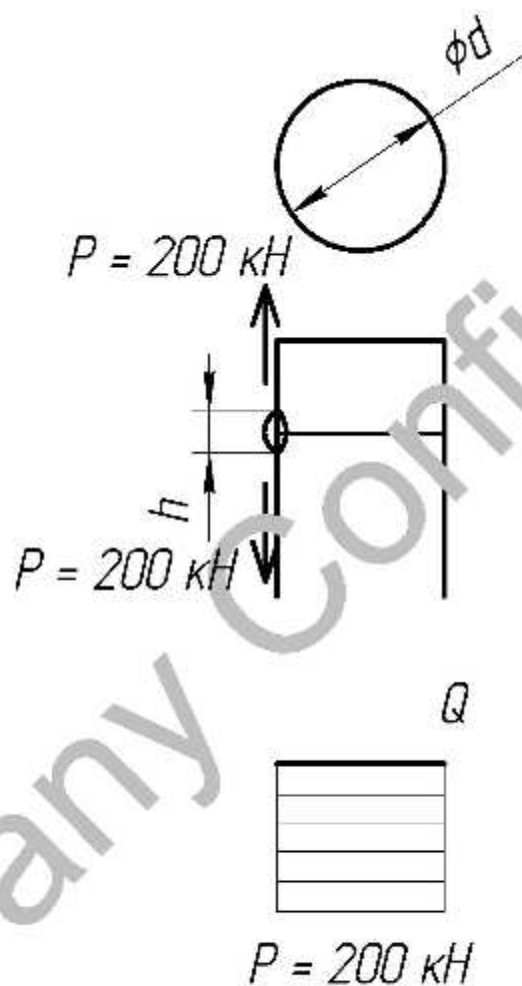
Для расчета сварного шва гидравлического цилиндра
